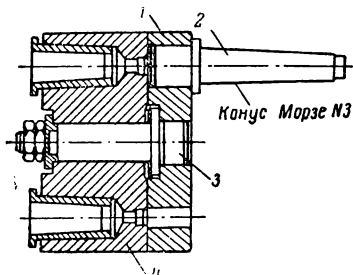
Специальная поворотная головка для закрепления четырех инструментов.
